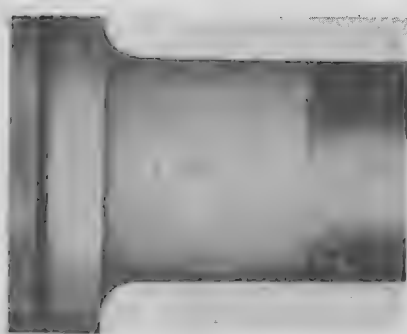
Трещина, выявленная травлением поверхности вала.
